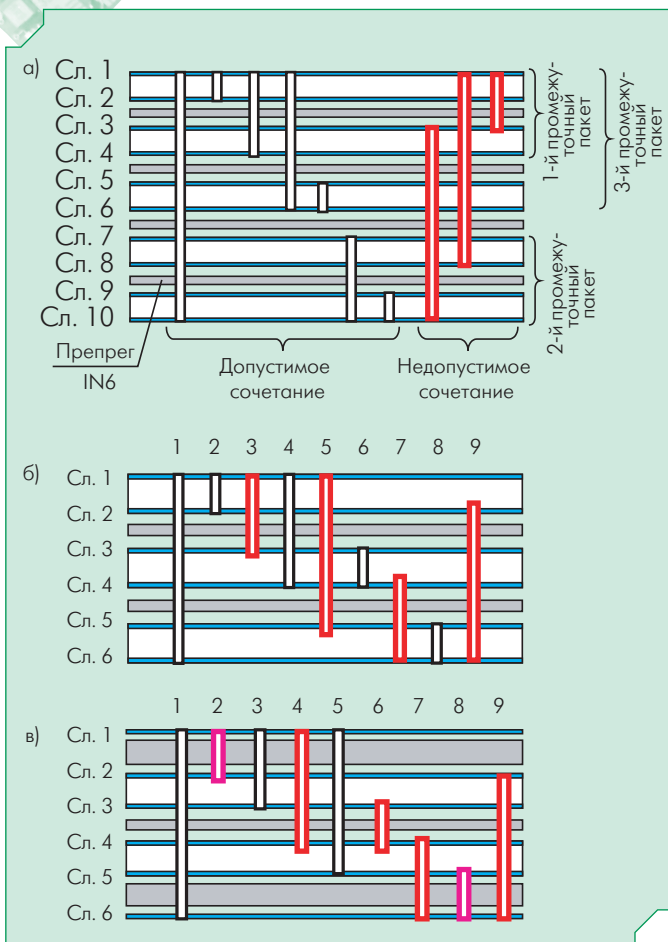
Конструкции 10- и 6-слойных плат из двухслойных ламинатов и препрегов
